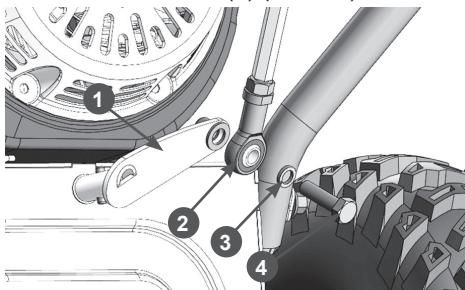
Установка тяги рычага переключения передач (нижний конец)
